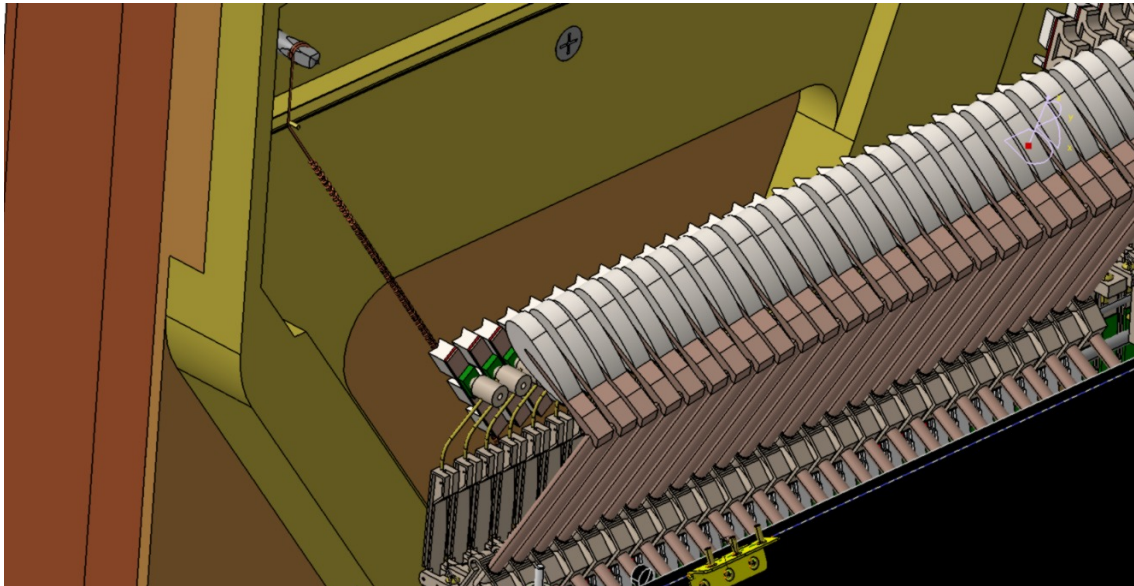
Cuerda y clavijero colocada en el mecanismo. Fuente: elaboración propia.
